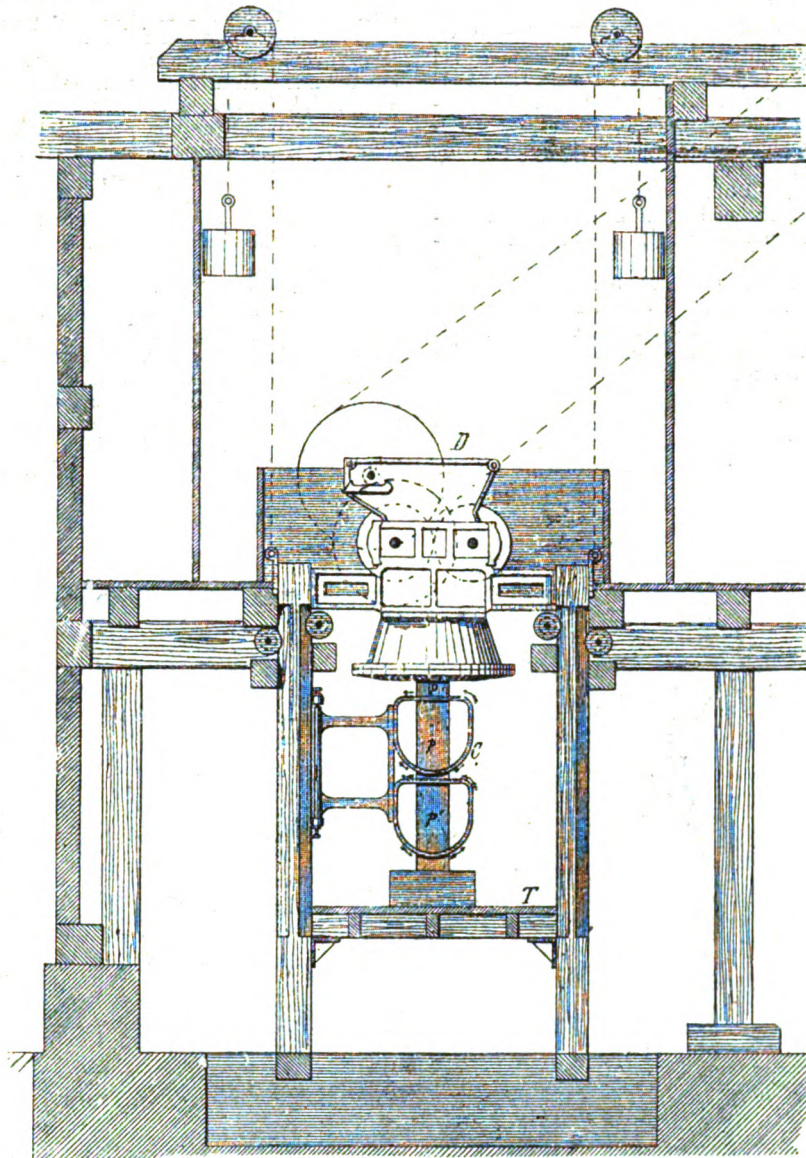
Aufriss einer verticalen Packet-Dachziegelpresse.
